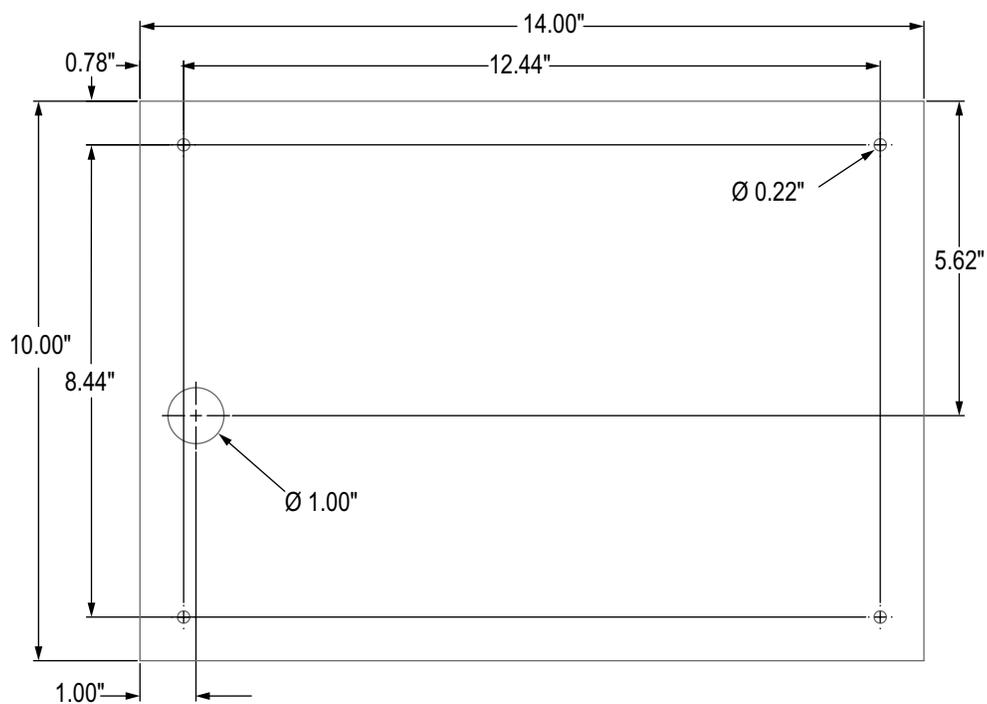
Dimensioni della versione da 12" con montaggio a pannello solo touch
